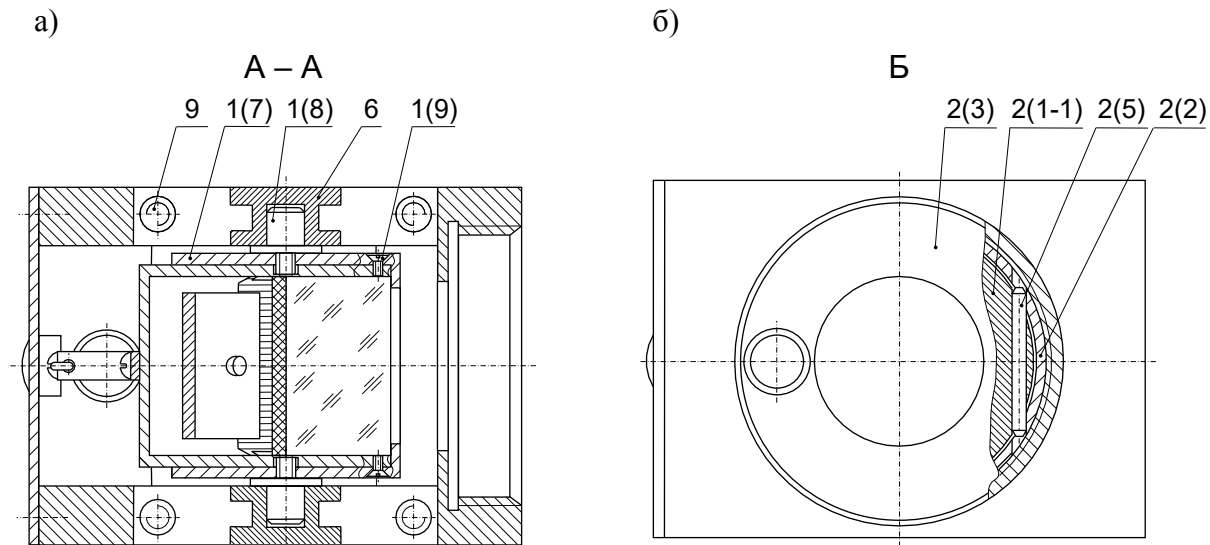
Конструкция механизма юстировки и крепления призмы АР-90°:
